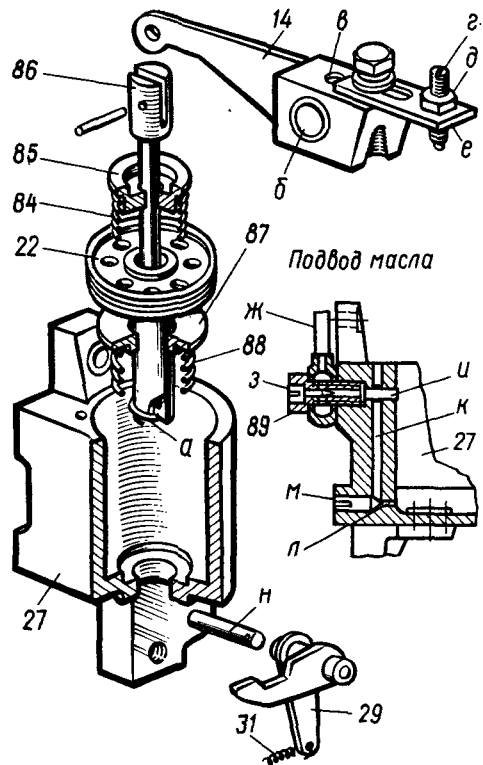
Компенсатор неравномерности хода: 84, 88 — пружины; 83, 87 — тарелки; 86 — штанга; 89 — штуцер (остальные обозначения общие с рис. 47)
